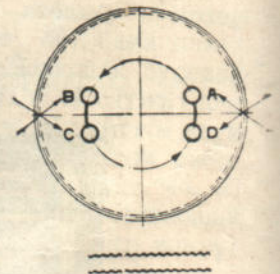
Передача от зубчатого колеса к верхнему коленчатому рычагу и от рычага к штанге в другом положении.
